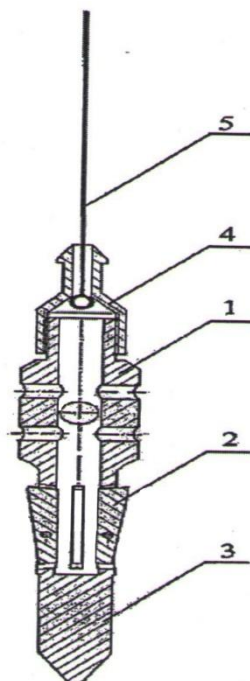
Ловитель забойного штуцера: 1 - корпус ловителя; 2 - захватные кулачки смещенного центра тяжести; 3 - направляющий толкатель; 4 - головка ловителя; 5 - скребковая проволока глубиномера
